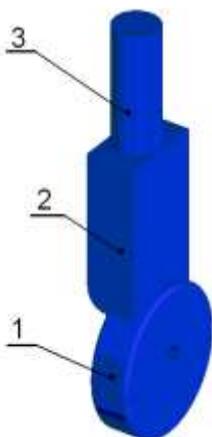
Исследованный узел отливки: 1-тепловой узел; 2-прибыль; 3-выпор
